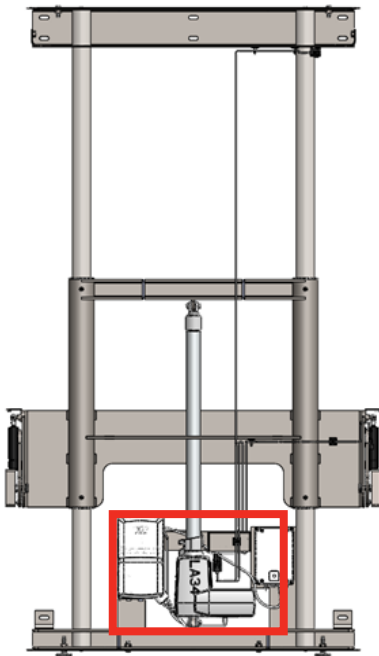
Emplacement du métier à tisser PCB et des connecteurs
